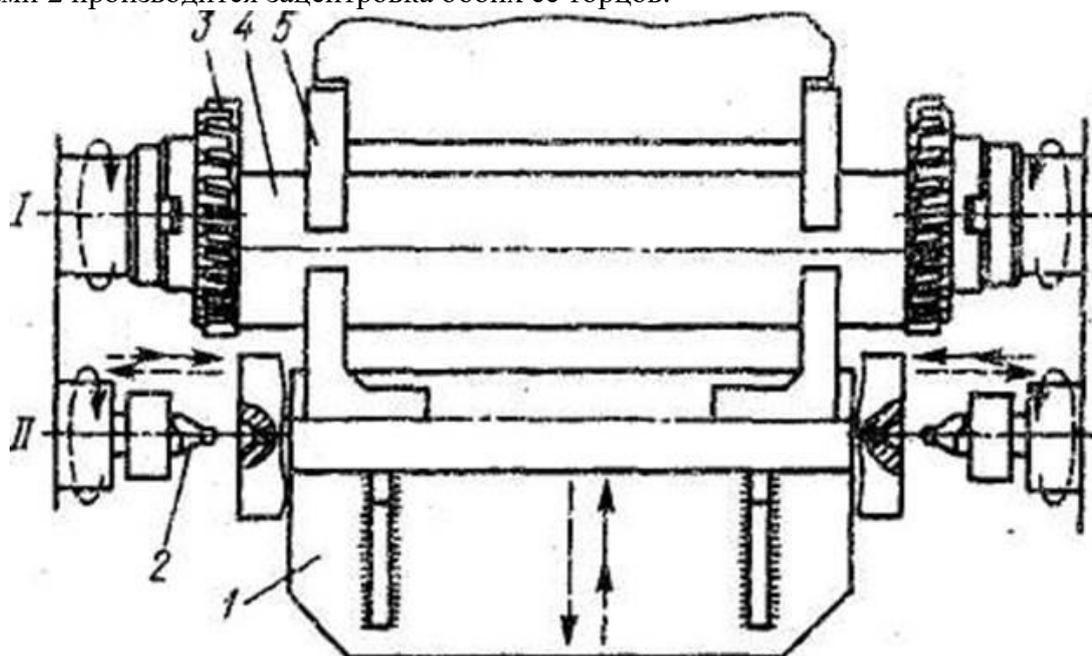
Схема работы фрезерно-центровочного полуавтомата.
